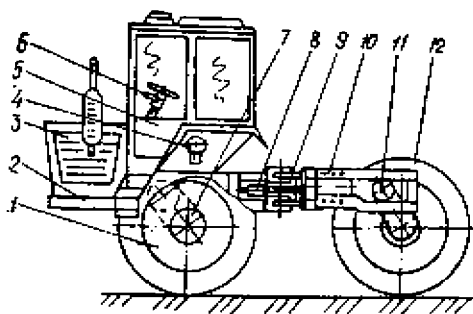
Схема лесохозяйственного колесного трактора: 1 – ведущие колеса; 2 – полурама; 3 – мотор-генератор; 4 – топливный бак; 5 – кабина оператора; 6 – система управления трактором; 7 – мотор-редуктор привода ведущих колес; 8 – электромеханизмы; 9 – поворотное устройство; 10 – полурама; 11 – мотор-редуктор; 12 – задние колеса
